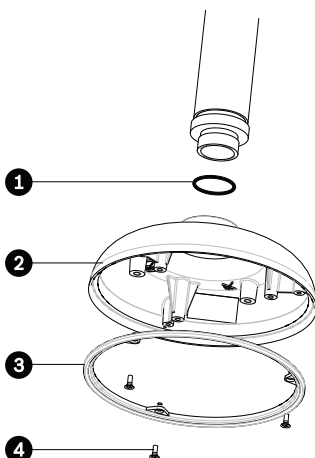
Colocação da junta circular e do anel de retenção para instalação exterior
